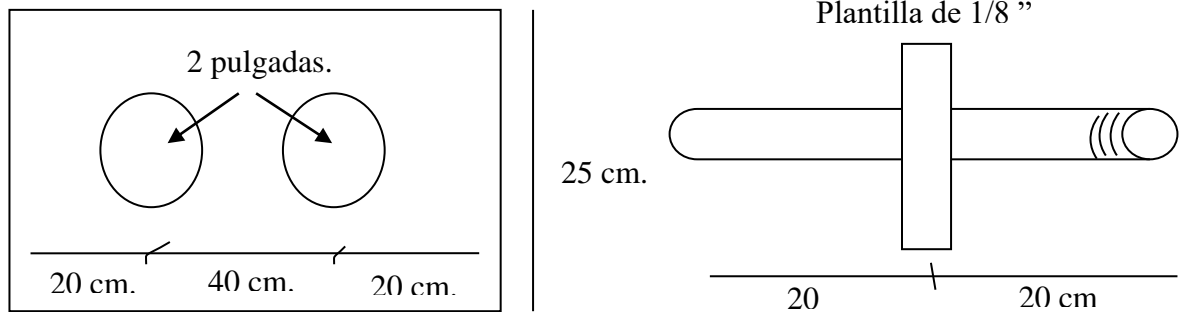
Diseño de la platina de desagüe del Tanque de Almacenamiento.
